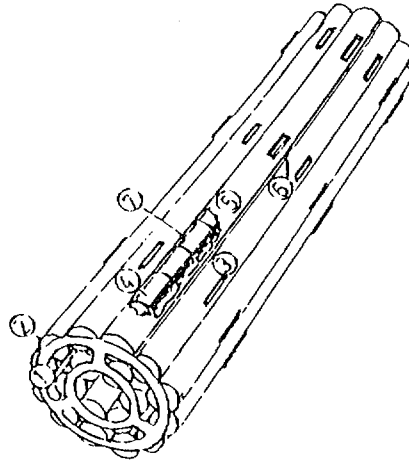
Berkas elemen bakar jenis HWR Candu tipe Pickering dan komponennya
